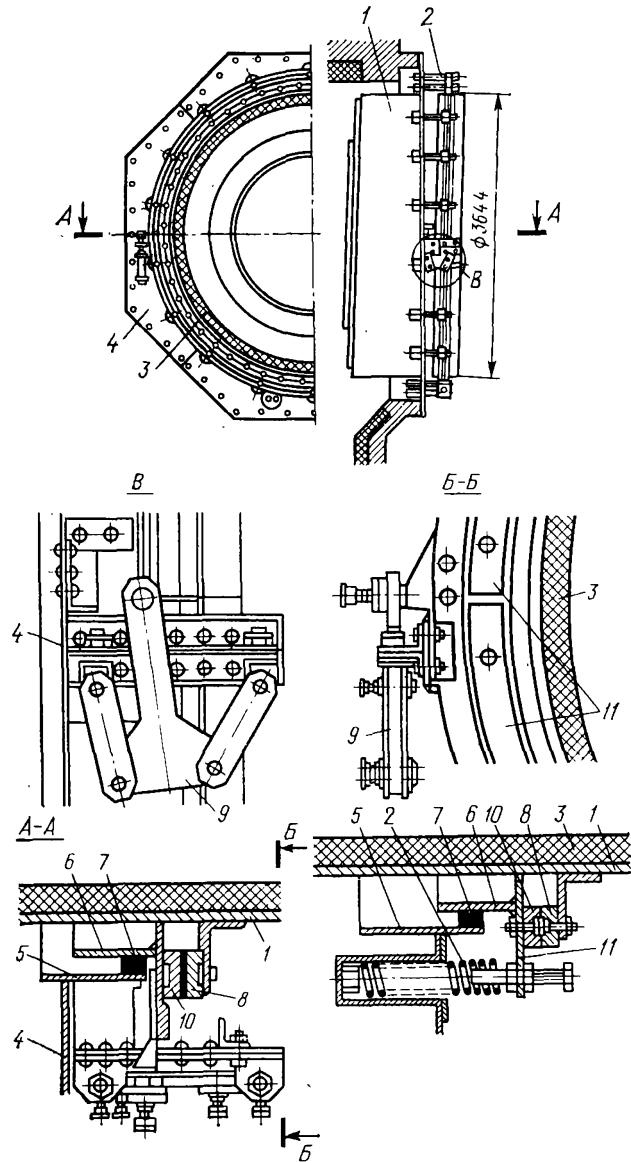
Устройство для уплотнения загрузочной головки вращающейся печи размером $3,6 \times 75$ м:
